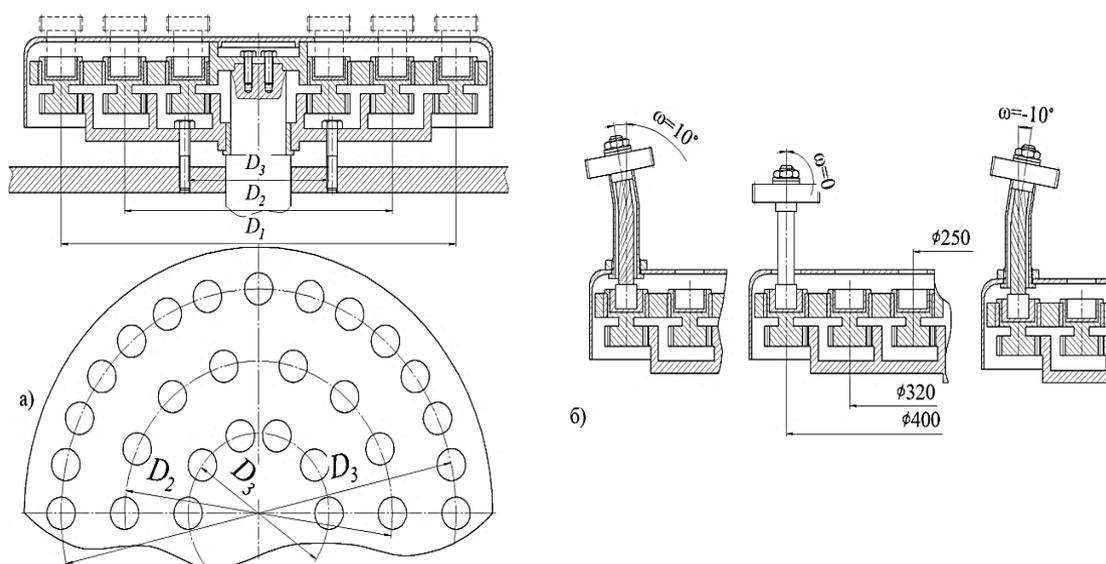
Схемы планетарного стола вакуумной камеры (а) и расположения зубчатых колес на планетарном столе (б) в процессе нанесения покрытий
